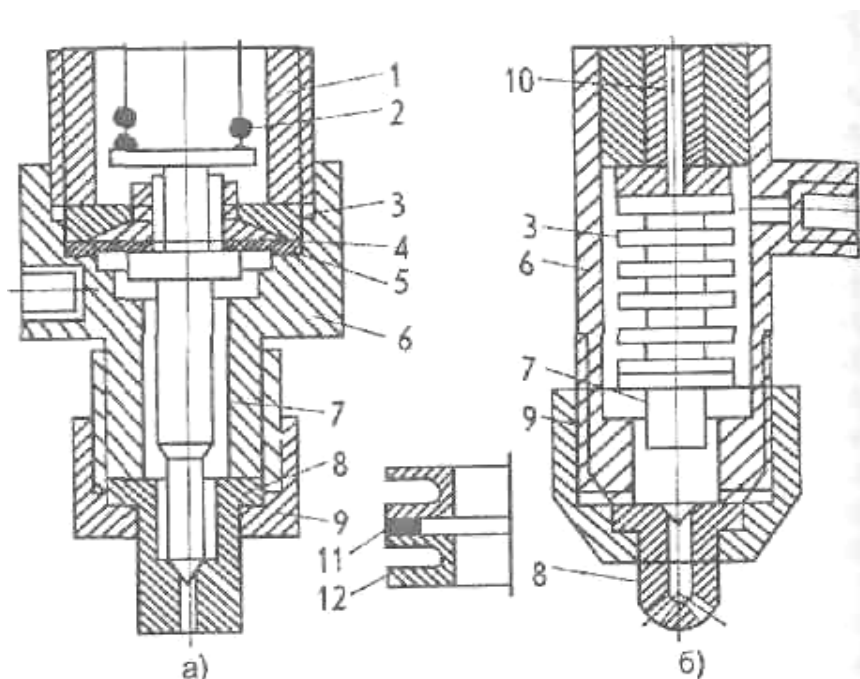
Мембранные форсунки: а - с плоской мембраной; б - с мембранной колонкой; 7 - штуцер; 2 - пружина; 3 - постель; 4 - гайка; 5 - мембрана; 6 - корпус форсунки; 7 - клапан; 8 - сопло; 9 - прижимная гайка; 10 - канал; 11 - кольцо; 12 - стальная пластина
